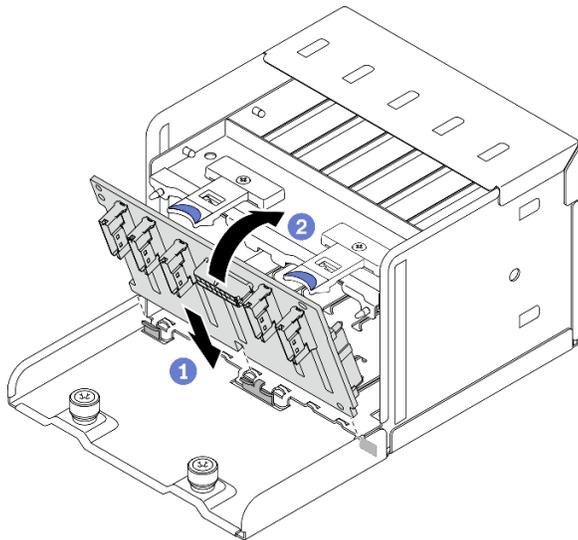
Installation du fond de panier d'unité 2,5 pouces
